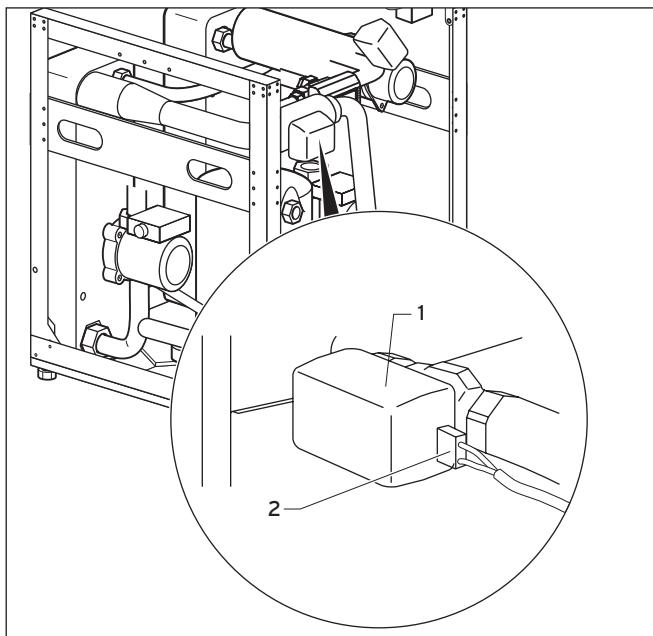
Клапан рассольной смеси с корпусом двигателя
